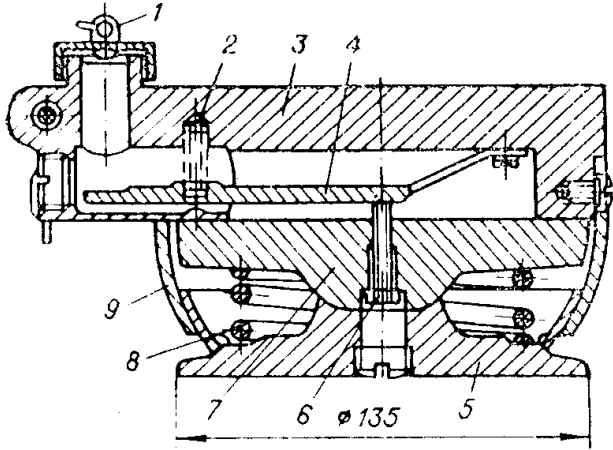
Конструкція механічного стійкового динамометра МСД:
